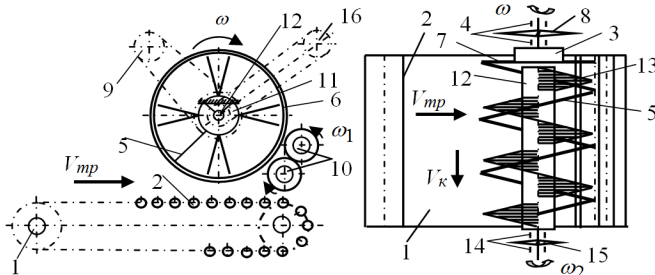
Схема удосконаленого базового АТОКРО: 1 – транспортер; 2 – пруток; 3 – шнек; 4 – опора шнека; 5 – виток; 6 – труба; 7 – фланець; 8 – ведена зірочка шнека; 9 – привод шнека; 10 – відминальні вальці; 11 – очисний вал; 12 – труба очисного вала; 13 – очисні пружні елементи; 14 – опора очисного вала; 15 – ведена зірочка очисного вала; 16 – привод очисного вала
